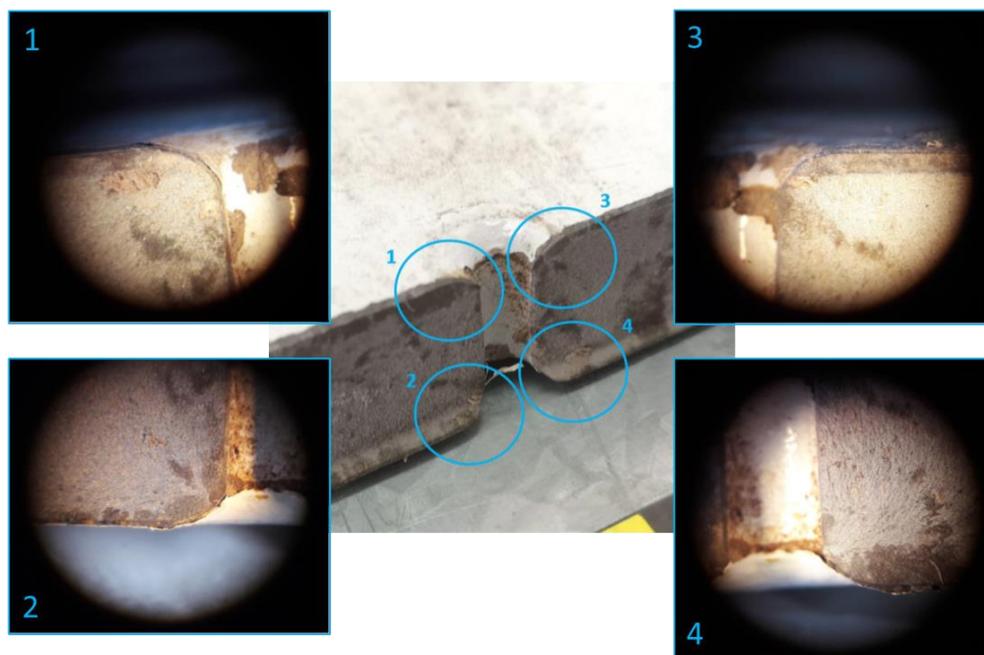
Plano de rotura de la ballesta y áreas de concentración de tensiones
